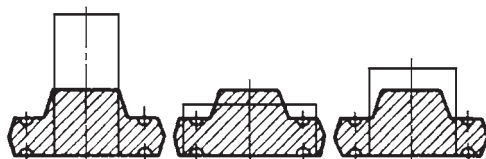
Выбор диаметра заготовки для поволоков с хвостовиком
